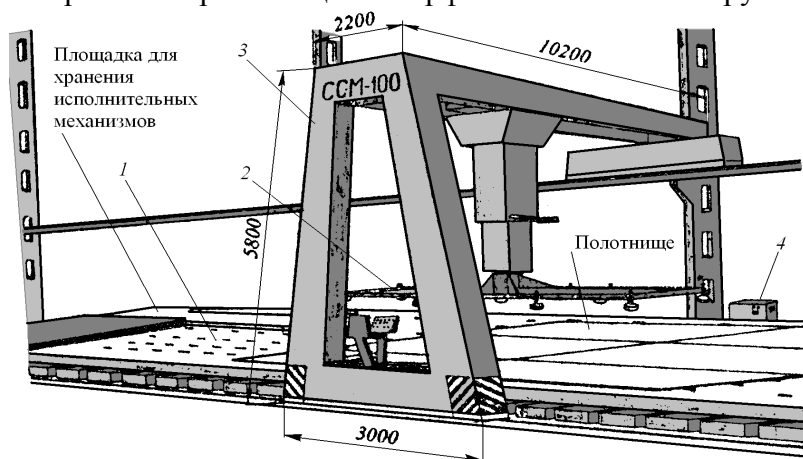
Общий вид многофункционального сборочно-сварочного манипулятора для изготовления плоских секций:
